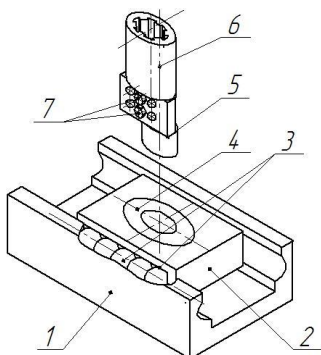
Ексцентриковий механізм: 1 – корпус; 2- повзун; 2 – кульки підшипника; 4 – підшипник; 5 – ексцентрик; 6 – вал-хвостовик; 7 - болти
